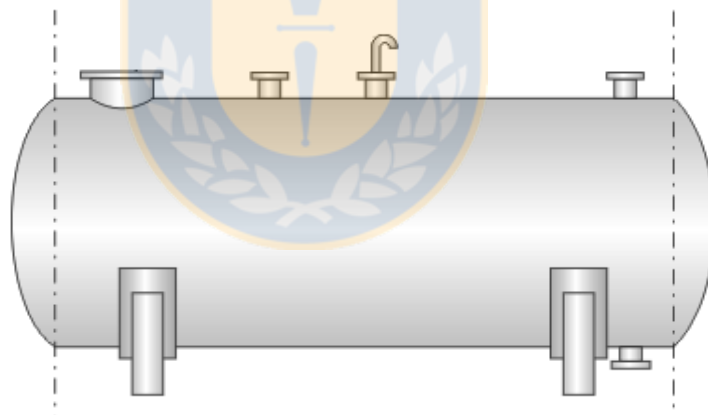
Estanque de almacenamiento horizontal. Fuente: elaboración propia.
